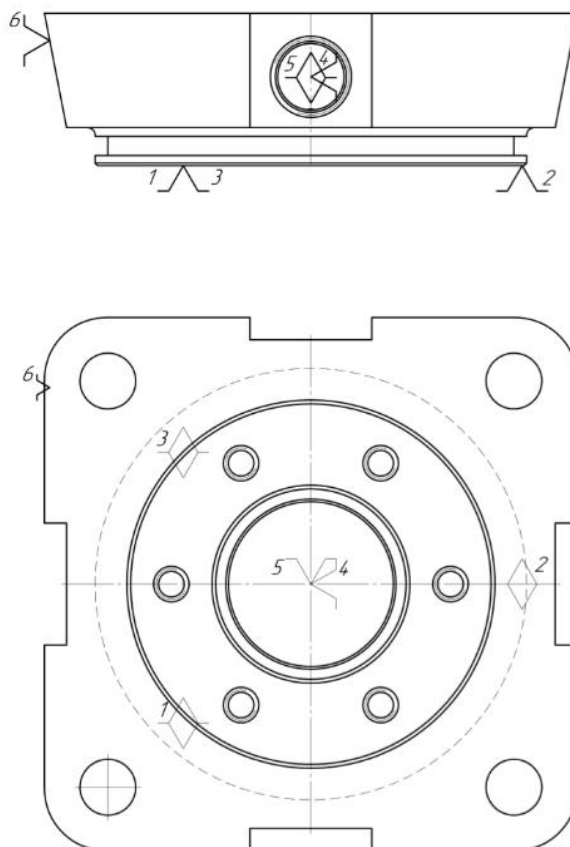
Схема базування деталі «Корпус» по ЗТБ 2.
